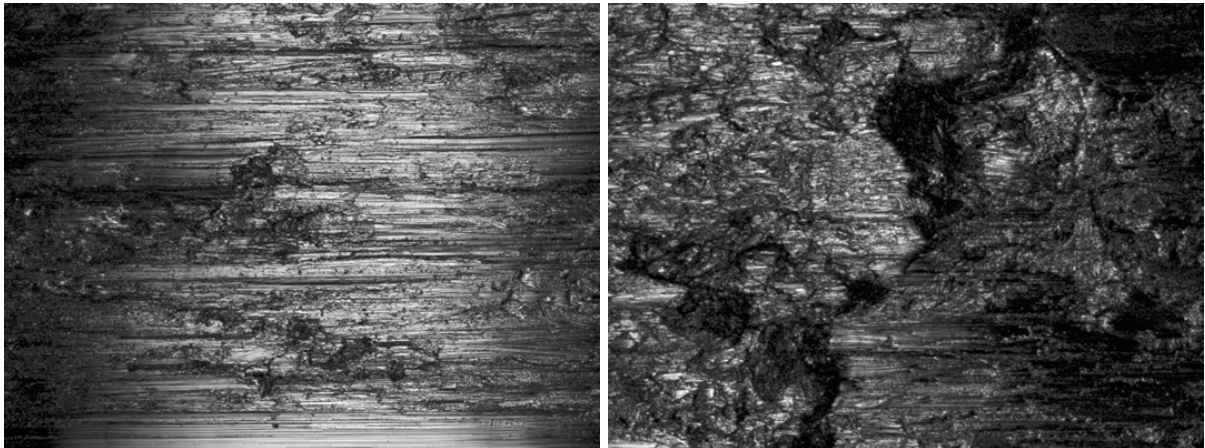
LSM-Aufnahme von der Bohrungsfläche. Im linken Bild sind die einzelnen Bohrriefen erkennbar. Die Rauigkeit ist in diesen Bereichen am geringsten. Im rechten Bild sind die einzelnen Riefen kaum sichtbar. Stattdessen sind Ausbrüche bzw. Verschweißungen des abgetragenen Materials mit der Bohrungswand sichtbar.
